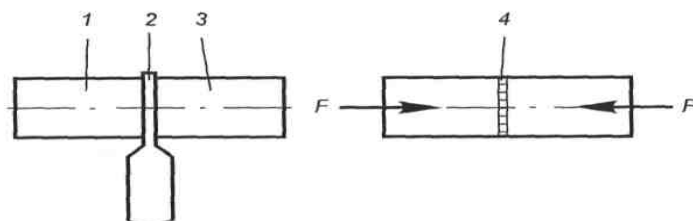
Схема зварювання нагрітим металевим інструментом: 1,3 – заготовка; 2 – металева пластинка; 4 – зварний шов; F – сила
